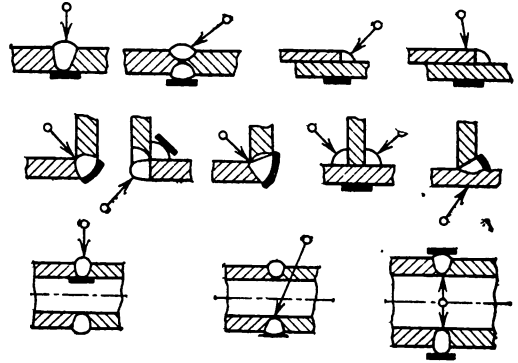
Схемы просвечивания сварных конструкций
